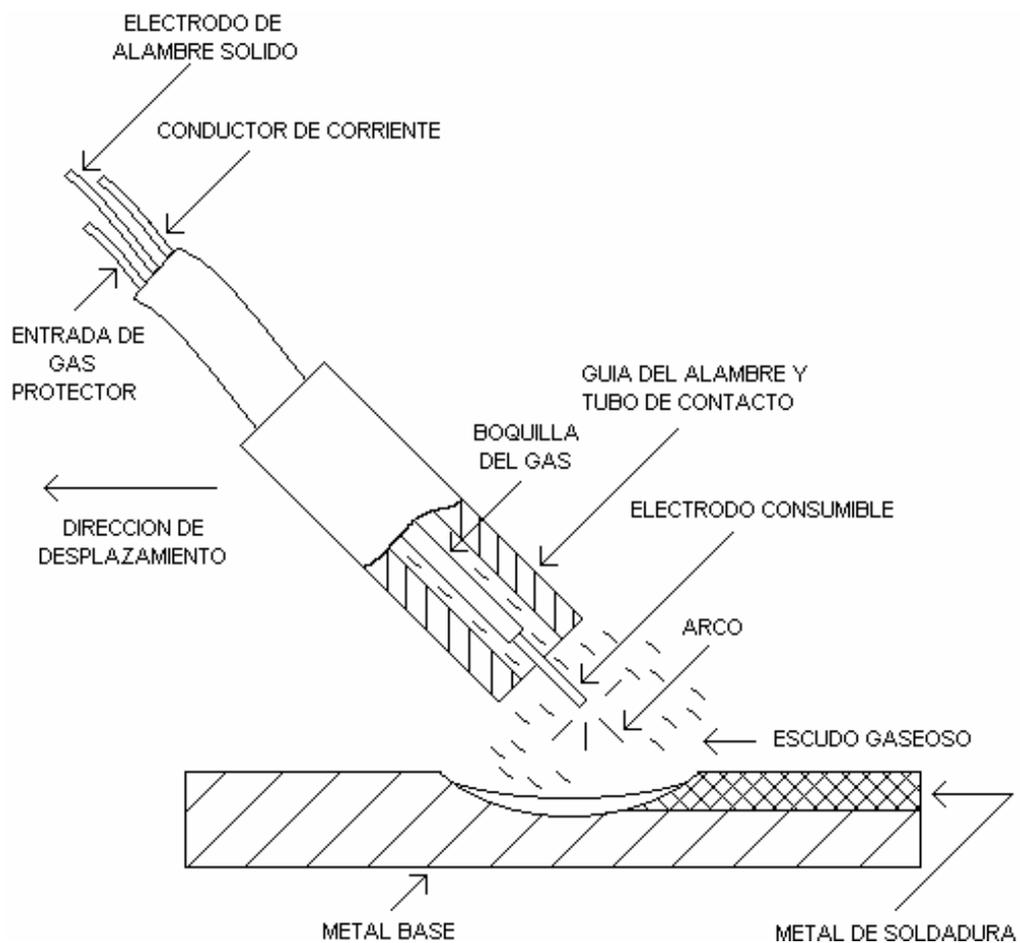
Proceso de soldadura por arco de metal y gas
